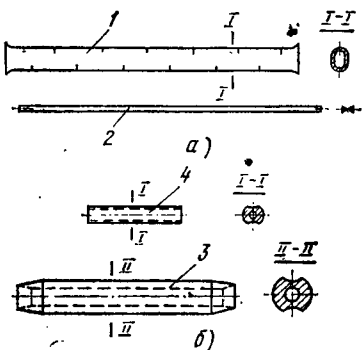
Овальный (а) и прессуемый (б) соединители:
